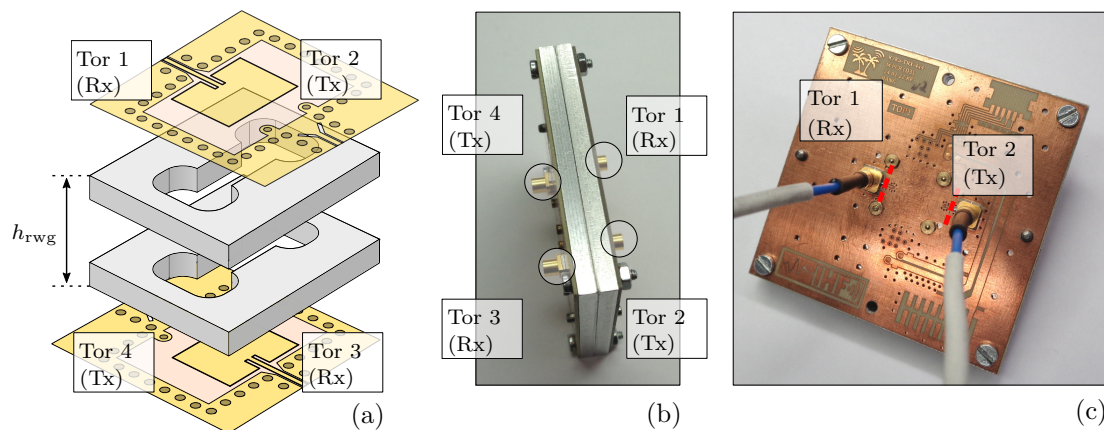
Vereinfachte Back-to-Back-Anordnung des PCB-Hohlleiter-Übergangs. (a) Explosionsdarstellung, (b) Seitenansicht und (c) Draufsicht des hergestellten PCB-Hohlleiter-Verbands mit Referenzebenen (rot).
